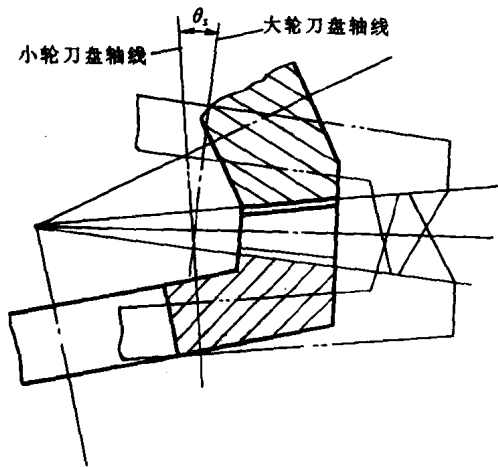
弧齿锥齿轮和准双曲面齿轮的加工
